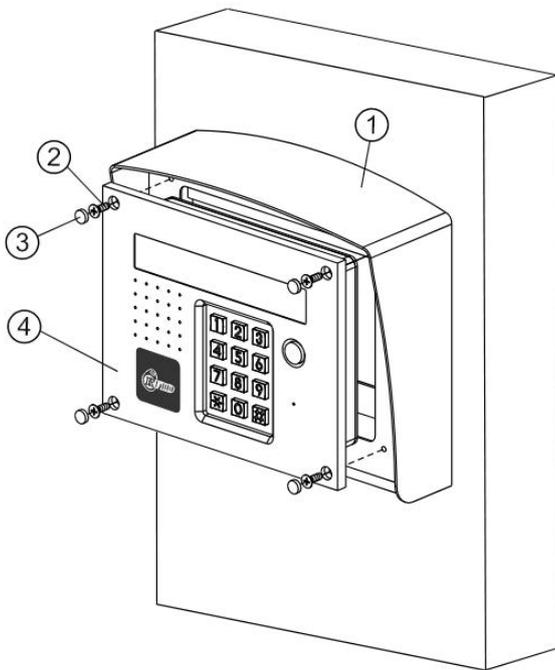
Установка блока вызова на неподвижной части металлической двери
